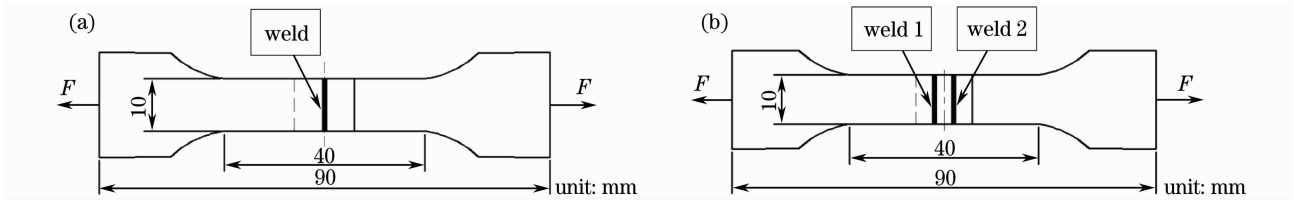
拉伸试验标准试样。(a)单焊缝,(b)双焊缝
